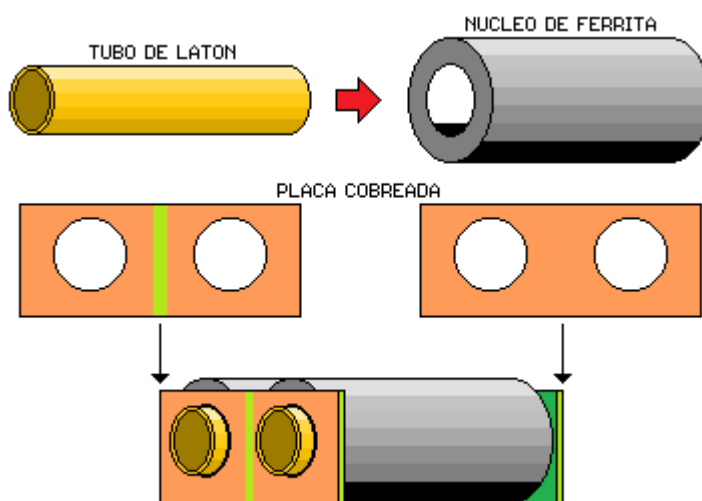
Detalles constructivos de los transformadores de banda ancha.
